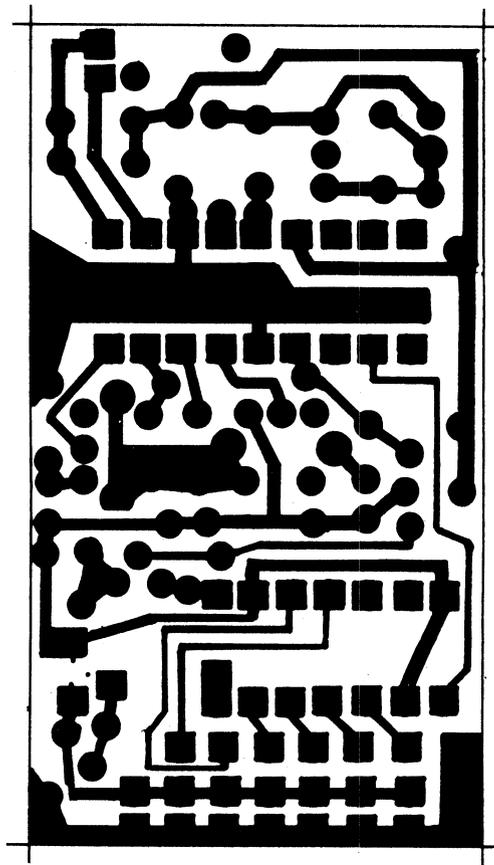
Négatif du plan de masse du RX 1872 B.
